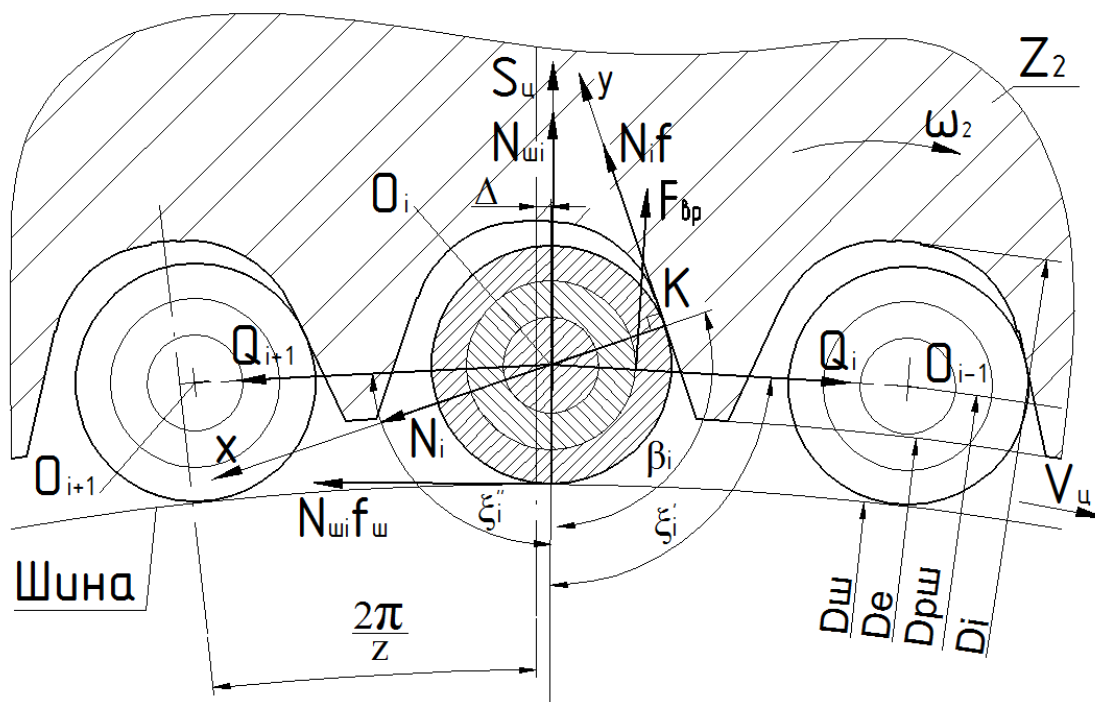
Шарниры цепи в зацеплении с ведомой звездочкой
